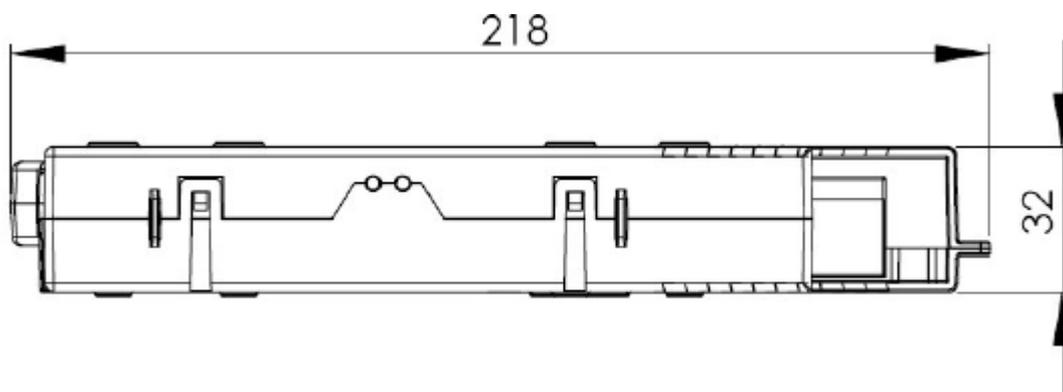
Dimensões do Módulo de Medição - Vista inferior
